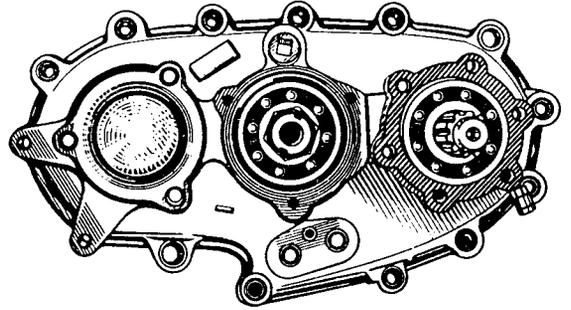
Verteilergetriebewellen, im Gehäusedeckel eingebaut
